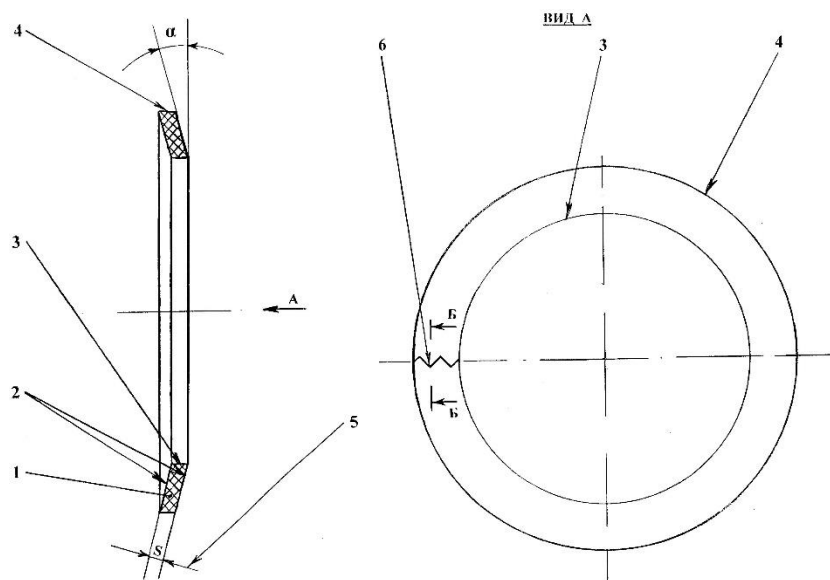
Уплотнительное кольцо: 1 –уплотнительное кольцо; 2- торцевая поверхность; 3,4 – внутренняя и внешняя цилиндрическая поверхность; 5 – толщина кольца; 6 – зубчатые разрезы
